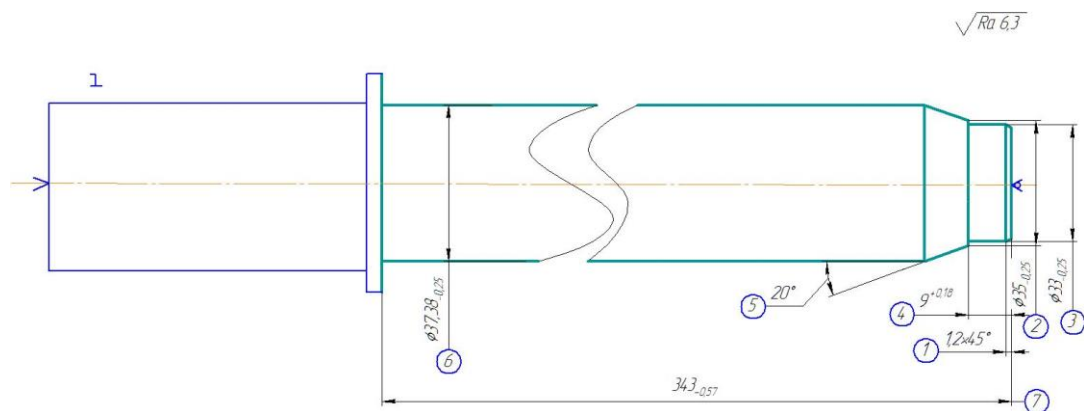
Закріплення заготовки в патроні та в обертовому центрі
